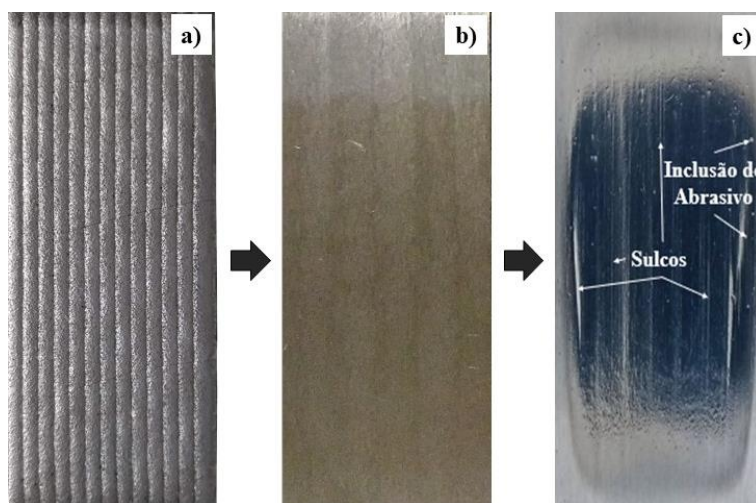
Etapas seguidas: a) deposição, b) revestimento e c) superfície desgastada.
